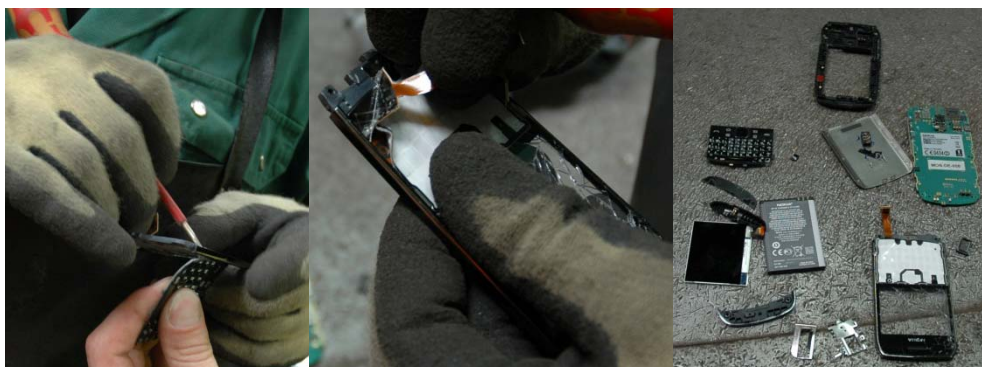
Entfernen des Tastaturfeldes durch Lösen der Klickverbindung (links); flächig verklebtes Tastatur-Kontaktfeld in Gehäusefront (Mitte); Einzelteile des Gerätes (rechts)
